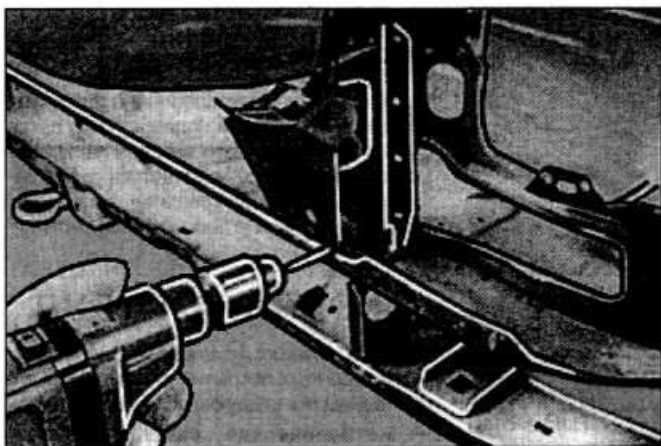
Высверливание сварных точек для снятия задней поперечины пола
